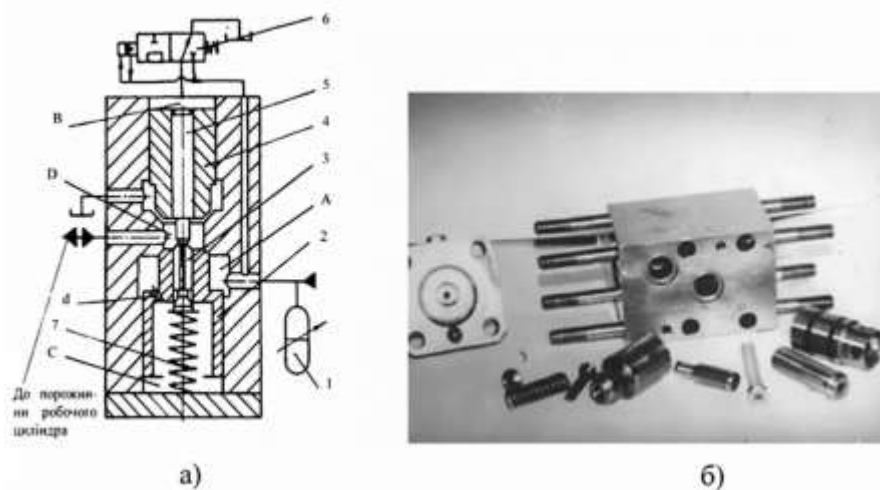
Віброзбуджувач типу А2К1-БК2: а) конструктивна схема; б) загальний вигляд: 1 – акумулятор; 2 – впускний клапан; 3 – сервоклапан; 4 – випускний клапан; 5 – штовхач; 6 – клапан; 7 – пружина; А, В, С, D – порожнини; d – отвір
